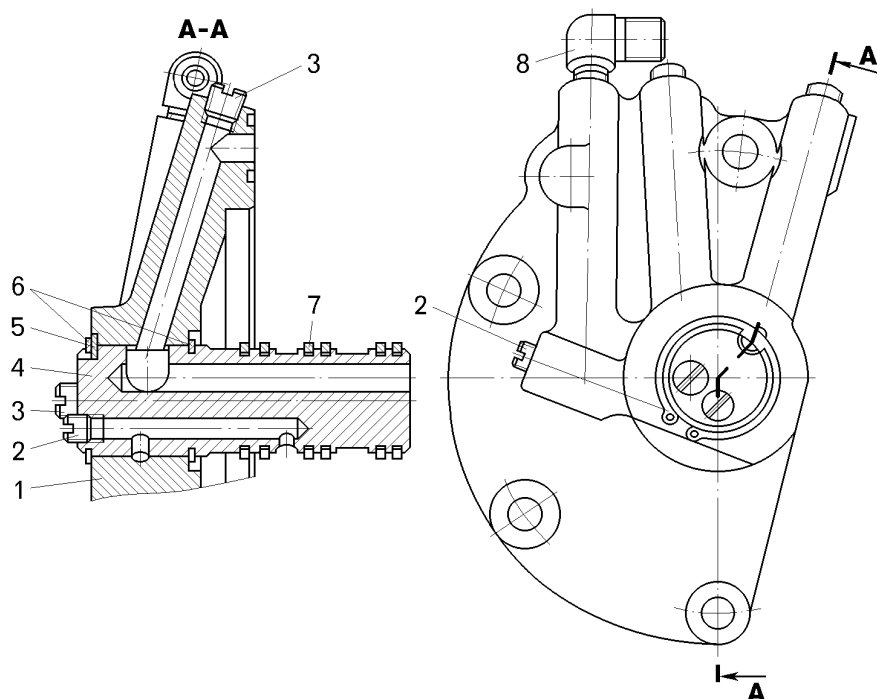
Крышка реверсивного вала с распределителем:
